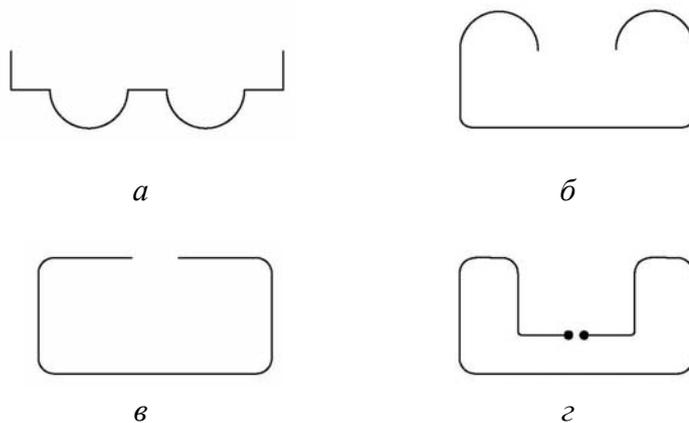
Форма гнутых профилей: а – открытые профили; б – полузамкнутые; в – замкнутые; г – сварные
